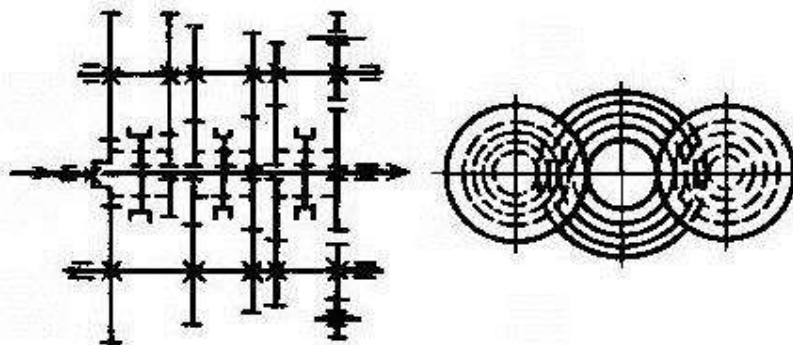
Кинематическая схема коробки передач с двумя промежуточными валами
